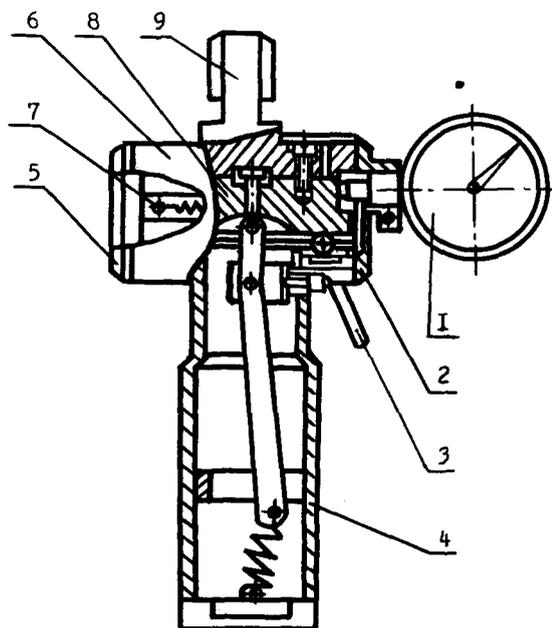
Приспособление для контроля смещения шпоночного паза:
